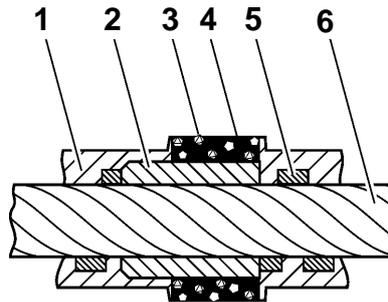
Cordão diamantado sinterizado Ø 11 mm
